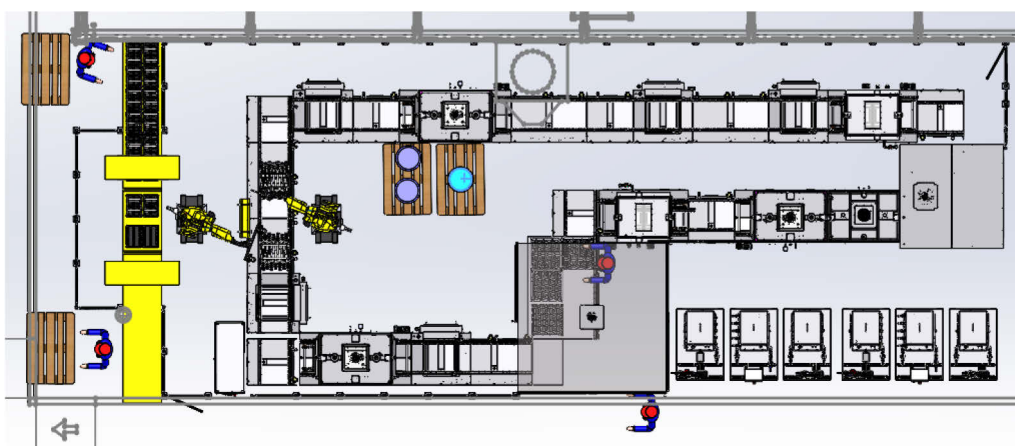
Layout mit Robotik, umlaufendem Korbtransport, Rissbewertung (unten Mitte) und modularem Wasserfiltersystem (unten rechts)
